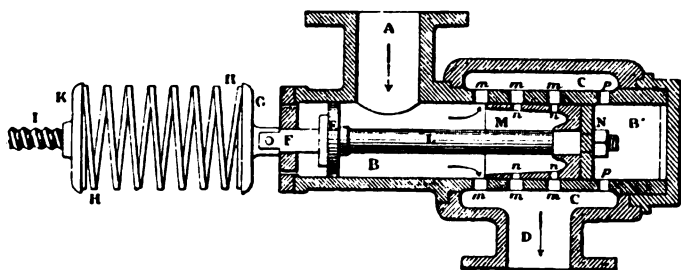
Régulateur de la machine à air comprimé du Saint-Gothard.
